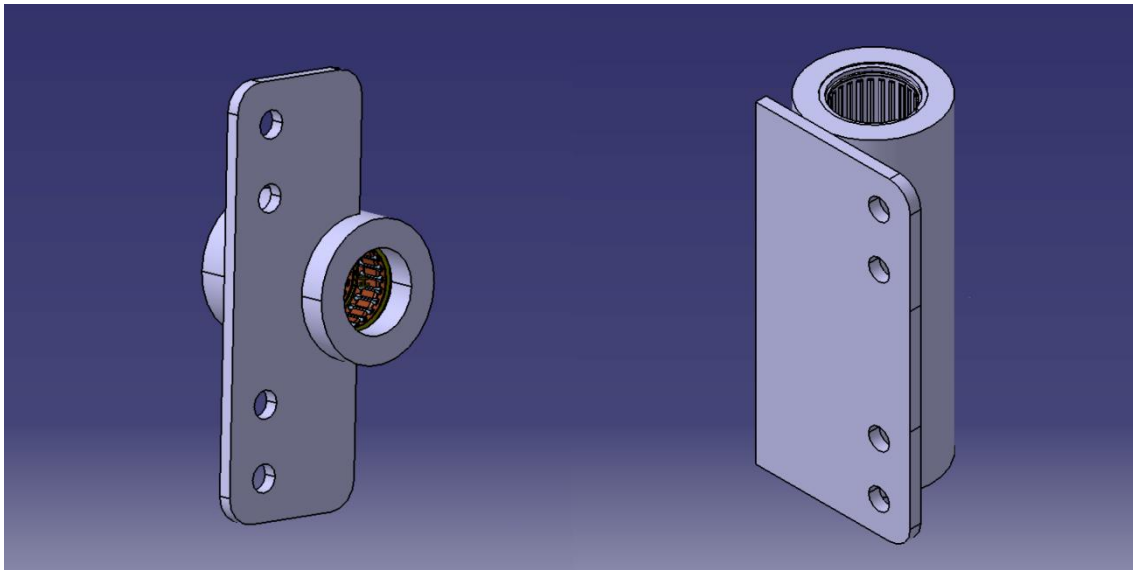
Piezas de giro soldadas y montadas
